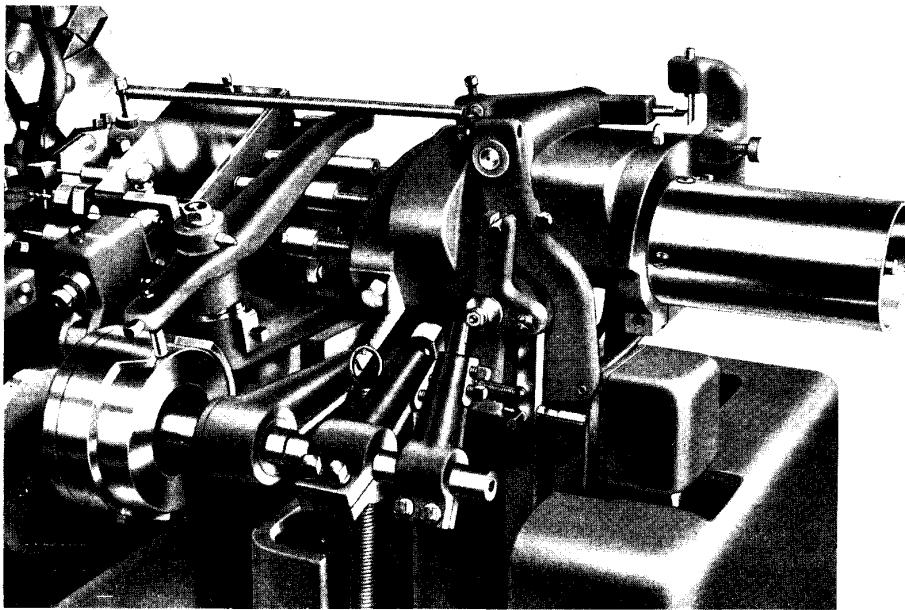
SCHWENKBARER WERKZEUGKOPF BP-U7
